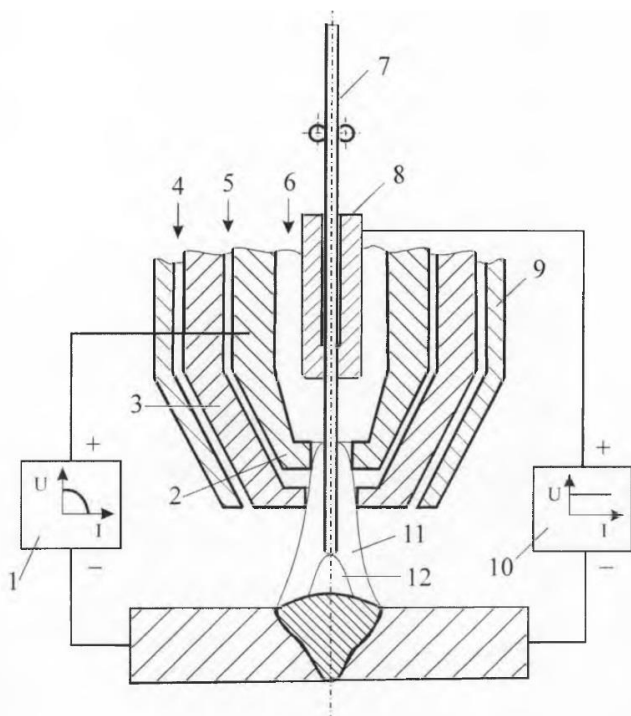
Схема плазменно-дуговой сварки плавящимся электродом:
